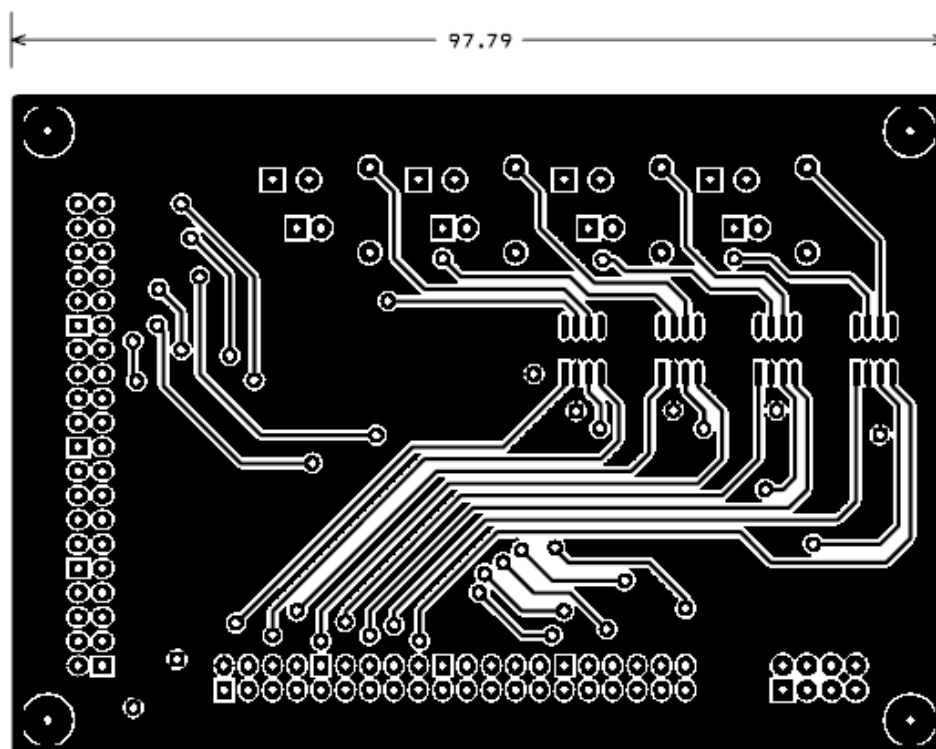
Face de "cima" da PCB (dimensões em milímetros).
